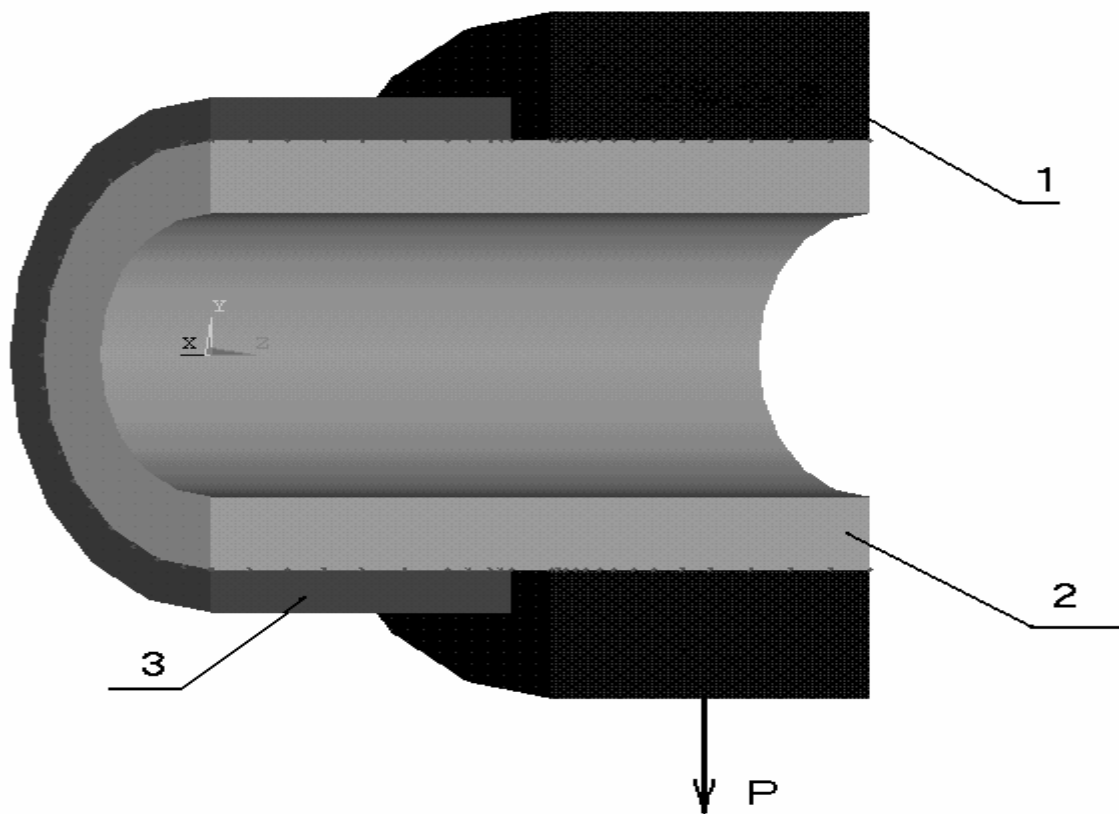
Схема нагружения поршневого пальца (1 - бобышка поршня; 2 – поршневой палец; 3 – головка шатуна).
